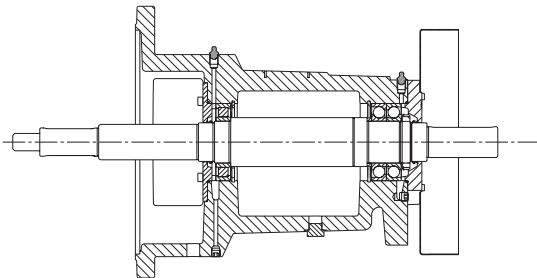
Корпус подшипников с открытыми роликовыми и двойными радиально-упорными подшипниками, смазываемыми через маслёнки для консистентной смазки
